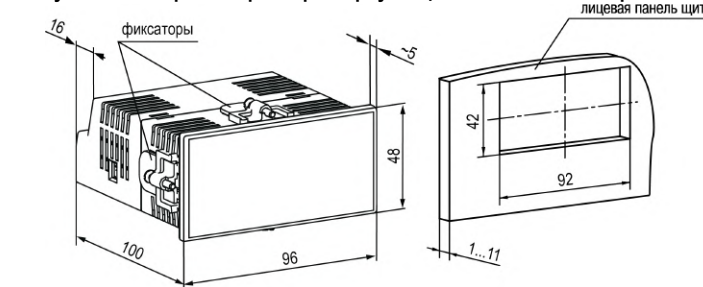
Габаритные размеры корпуса Щ2 и монтажного отверстия в щите
